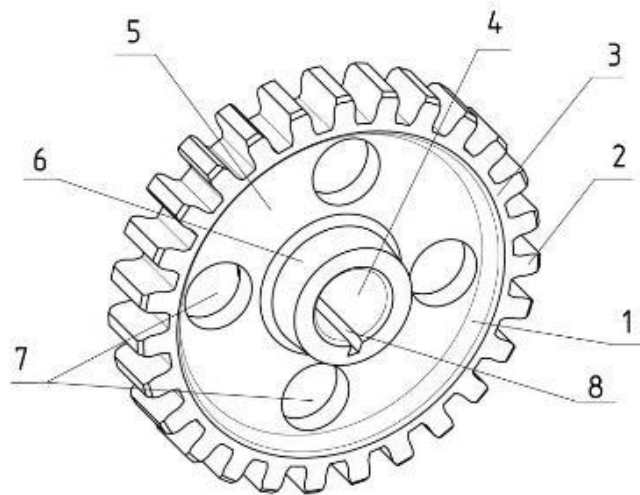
Строение зубчатого цилиндрического штампованного колеса: 1 – обод; 2 – зуб; 3 – венец; 4 – посадочное отверстие; 5 – диск; 6 – ступица; 7 – отверстие в диске; 8 – шпоночный паз
